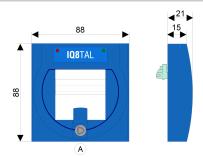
Abmessungen in mm Fig. 1: Dimensions in mm
